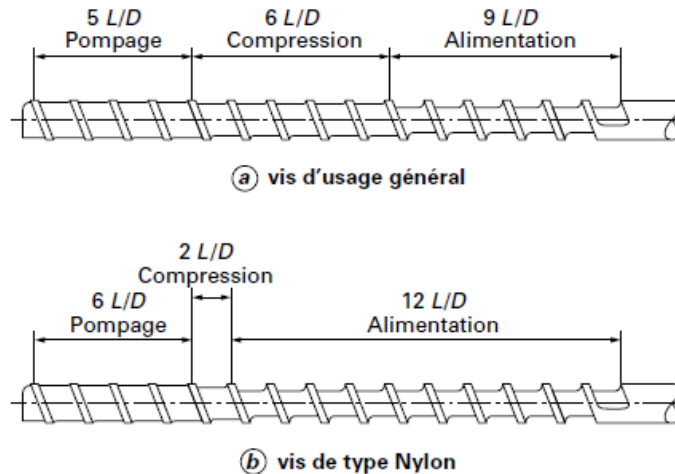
Profils de vis pour le moulage par injection du PEEK<sup>33</sup>.
